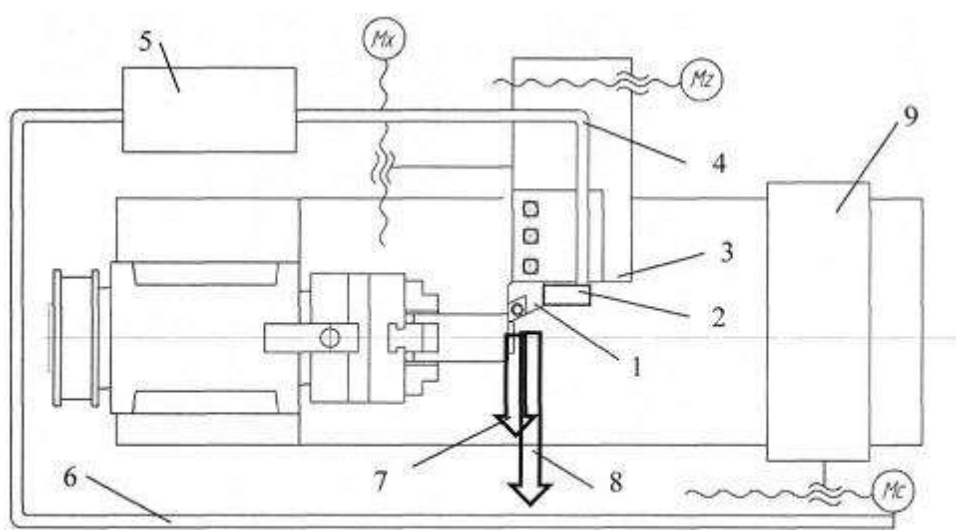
Спосіб динамічного управління коливаннями супорта верстата
